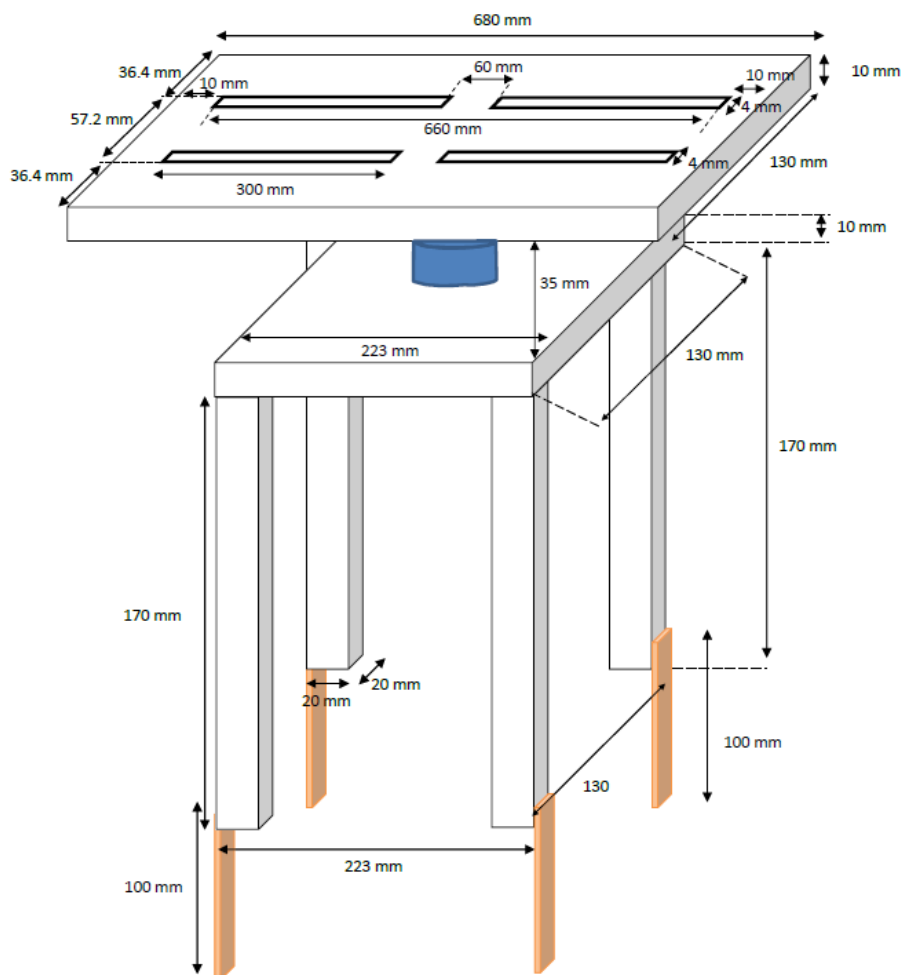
Plan du support de fixation du réseau transmetteur
